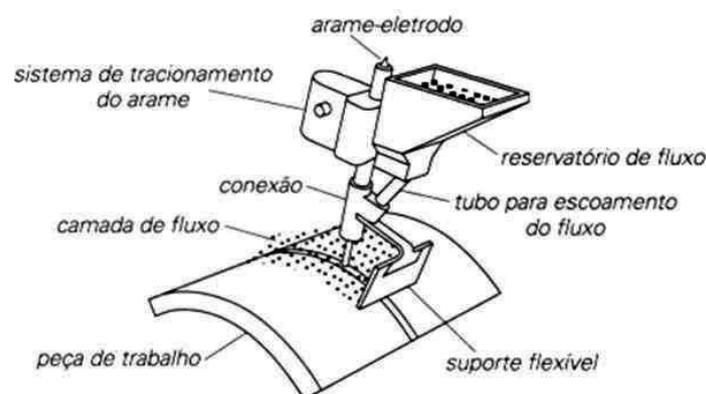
Soldadura por arco submerso Fonte: (Infosolda, 2013)
